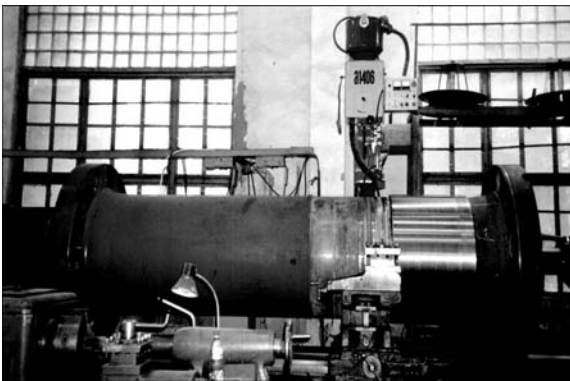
Модернизированная установка, созданная на базе токарного станка РТ-166, для наплавки и последующей механической обработки валов гидротурбин
